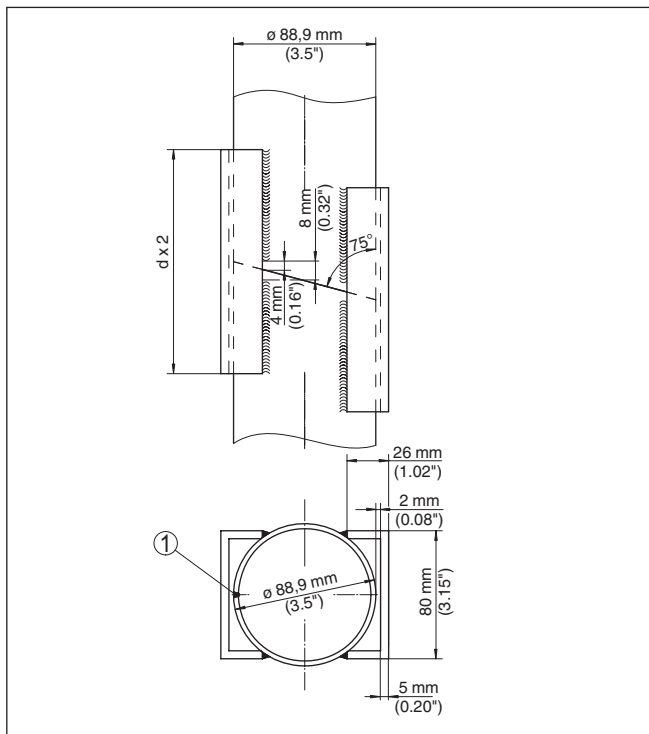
União soldada no prolongamento do tubo tranquilizador para diferentes exemplos de diâmetro
